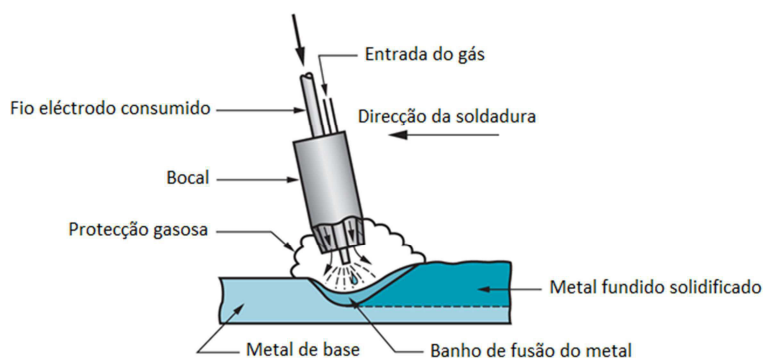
Soldadura MIG/MAG (GMAW) [FONTE: adaptado [58]].
